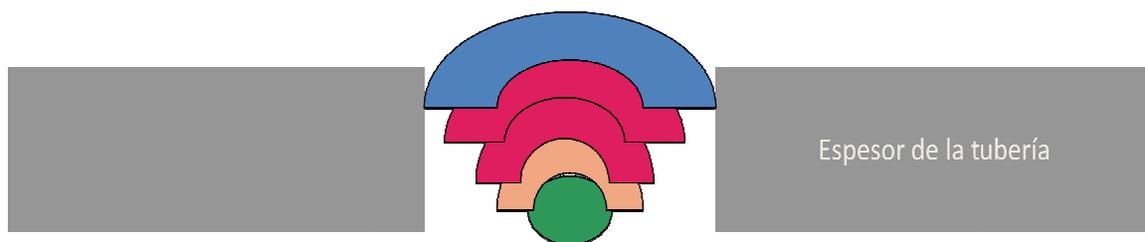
Diagrama de cordones de soldadura
